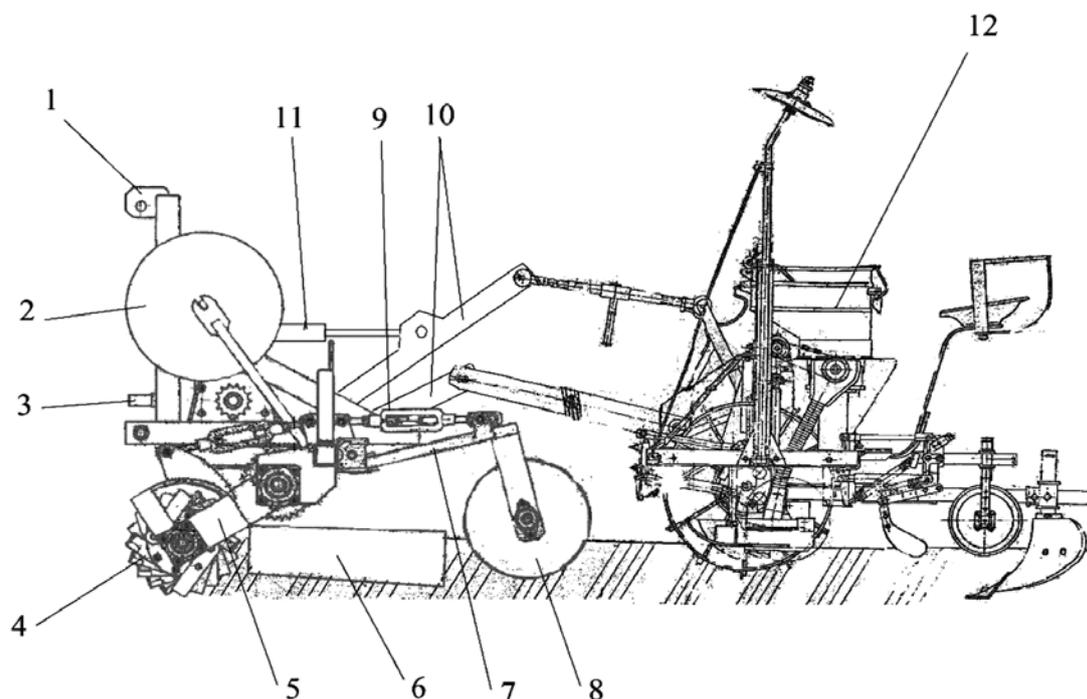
Комбинированная машина для предпосевного полосного фрезерования с одновременной укладкой шлангов капельного полива и возможностью посева: 1 – рама фрезы; 2 – бобина для шлангов капельного орошения; 3 – вал редуктора привода фрезы; 4 – ножевой барабан фрезы; 5 – кронштейн ножевого барабана; 6 – фартук гребнеобразователя; 7 – кронштейн гребне-уплотнительного катка; 8 – гребне-уплотнительный каток; 9 – талреп регулировки уплотнительного катка; 10 – навесное устройство для сеялки; 11 – гидроцилиндр навесного устройства для сеялки; 12 – сеялка
